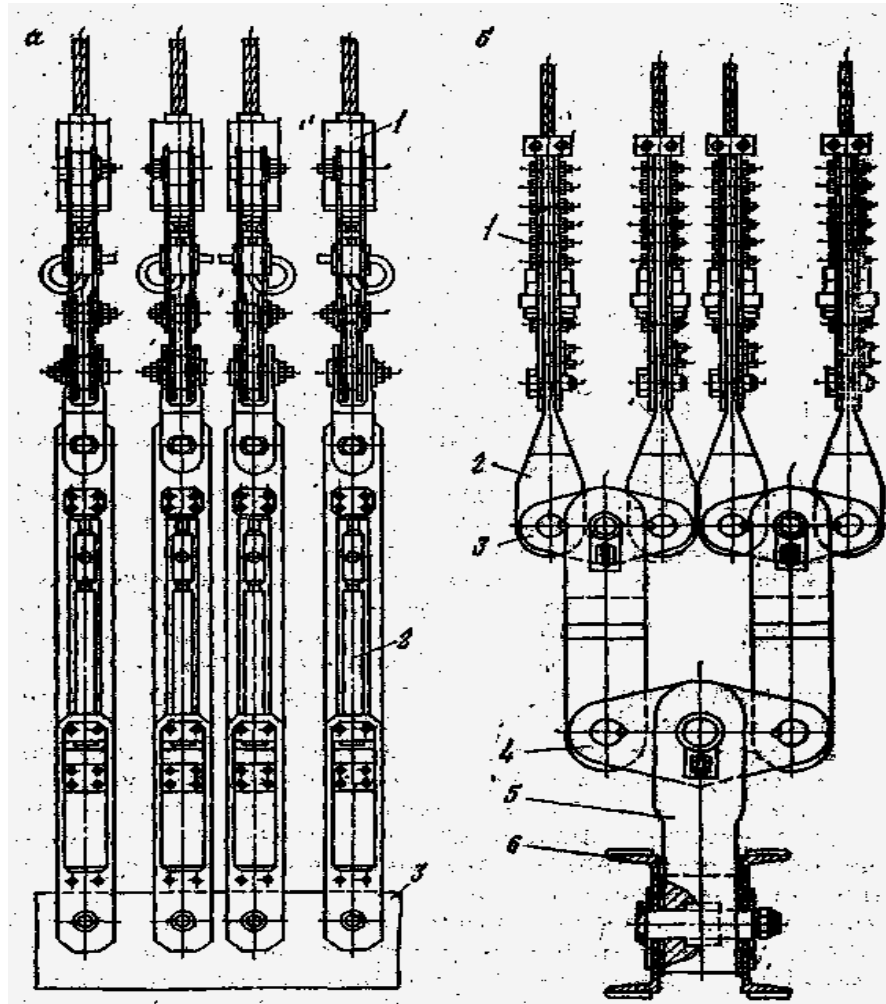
Підвісний пристрій КПК з клиновим коушем: 1 - коуш; 2 – верхня балка; 3 - стійки; 4 - шток підвіски
